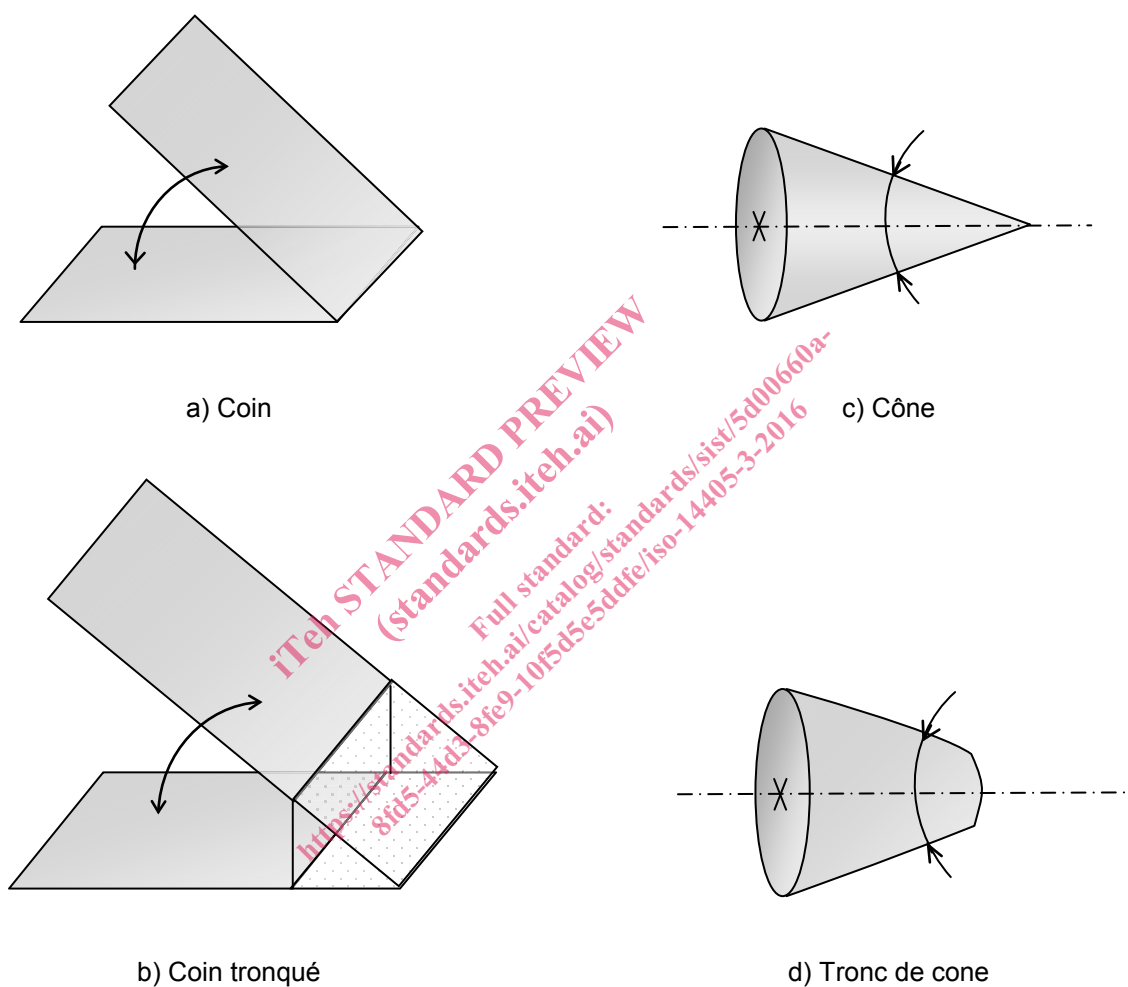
Exemples d'entités dimensionnelles de taille angulaire relatives à des surfaces
